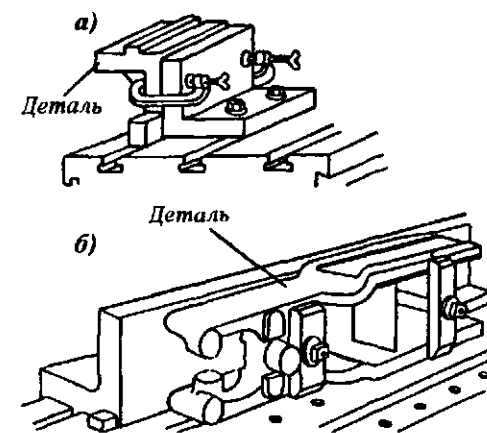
Схема установки и закрепления деталей на угольниках: а – стойка; б – кронштейн
